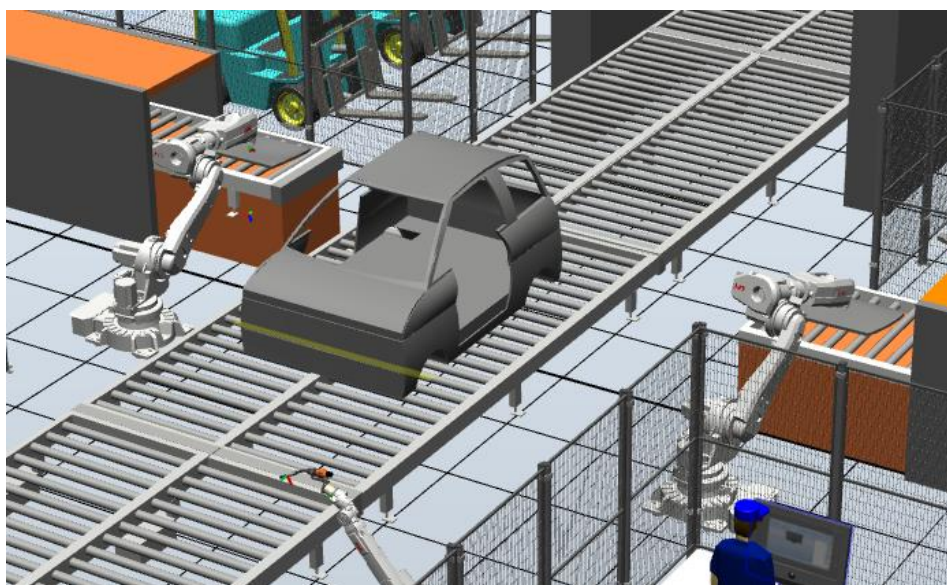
Recogida de las piezas mecanizadas en la segunda etapa.
